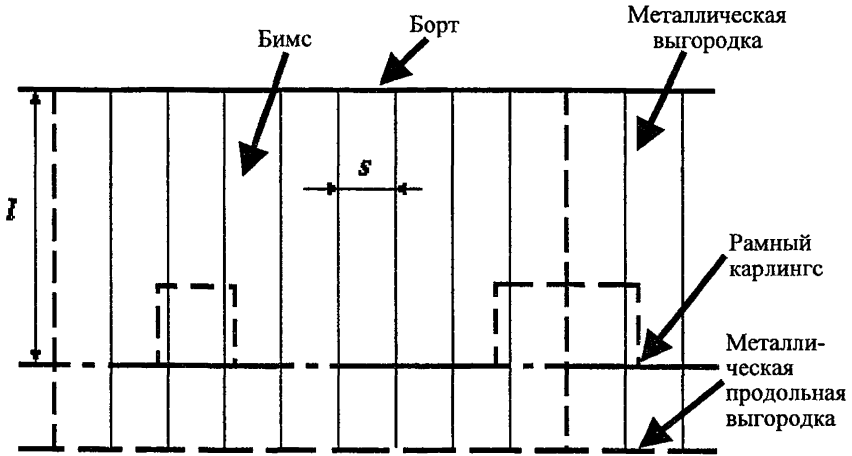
Типовая схема палубного перекрытия с поперечной системой набора.
